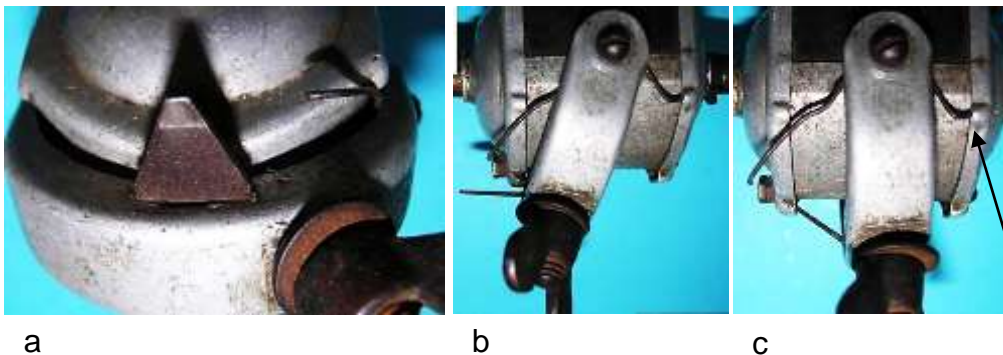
Kippvorrichtung: a) Sperrblech zur Arretierung der Betriebsstellung, b) Betriebsstellung, c) Ruhestellung
